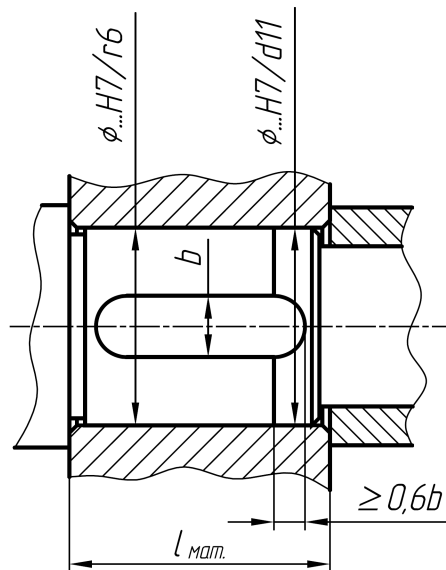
Виконання направляючої циліндричної ділянки вала
